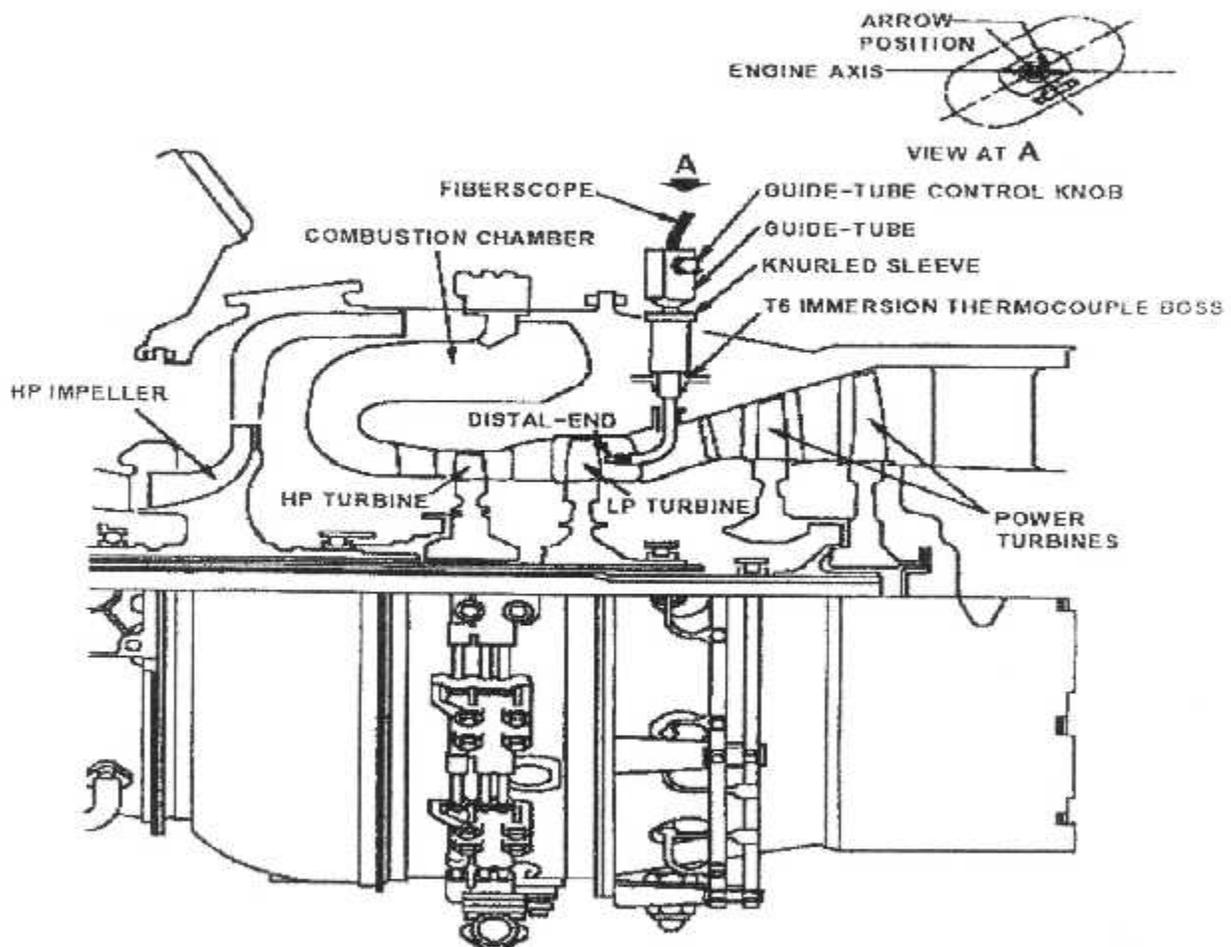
Inspection boroscopique du stator et des ailettes turbine HP.
